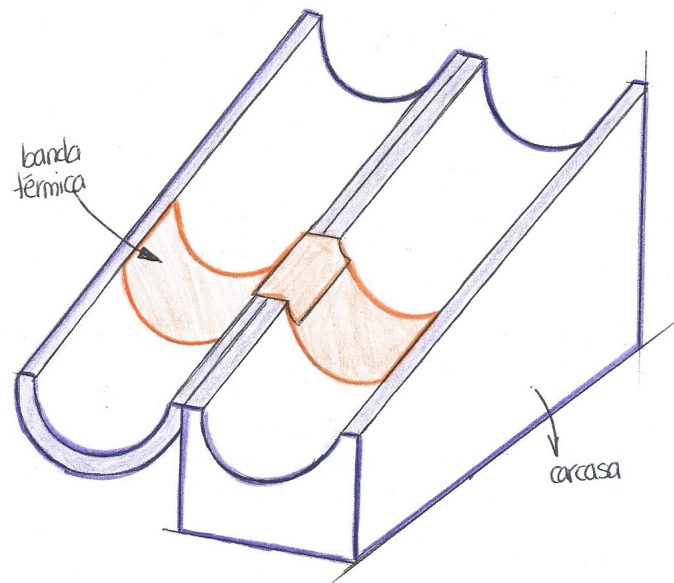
Tercera propuesta soporte brazo con manta eléctrica; Fuente propia
